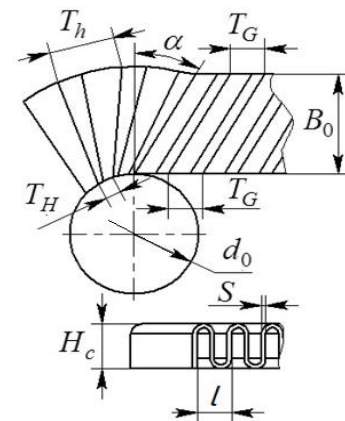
Розрахункова схема навивання гофрованої заготовки на оправу
